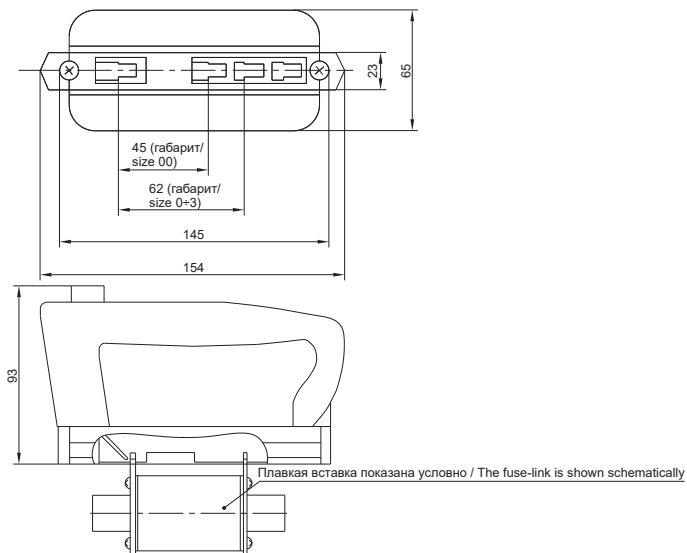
Габаритные размеры рукоятки съема плавкой вставки / Figure 3 – Overall dimensions of the fuse-link replacement handle
